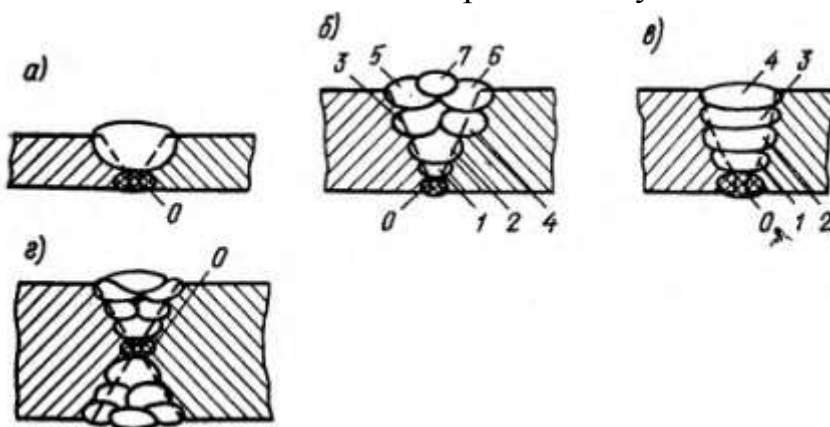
Сварка стыковых швов: формы поперечных сечений швов; (1-7) порядок выполнения слоев шва; (0) подварочный шов.
